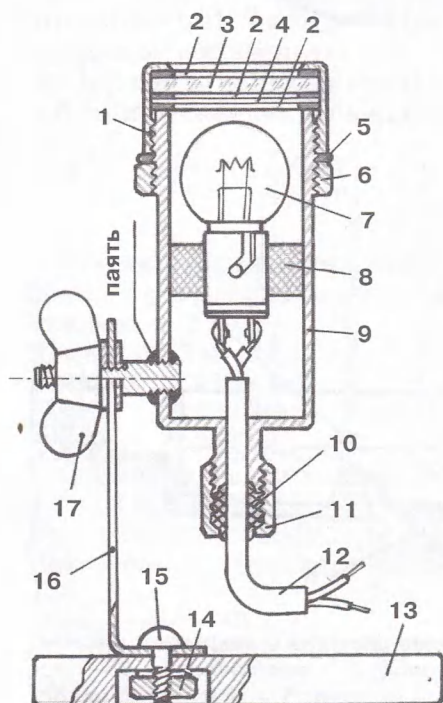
Герметичный источник света: 1 — резьбовая крышка; 2 — резиновая прокладка; 3 — стекло; 4 — пленка светофильтра; 5 — уплотнительное резиновое кольцо; 6 — прижимное резьбовое кольцо; 7 — электролампа; 8 — изолятор; 9 — корпус; 10 — втулка из сырой резины; 11 — уплотнительная накидная гайка; 12 — кабель питания; 13 — платформа; 14 — гайка; 15 — винт М6; 16 — кронштейн; 17 — гайка-барашек.
